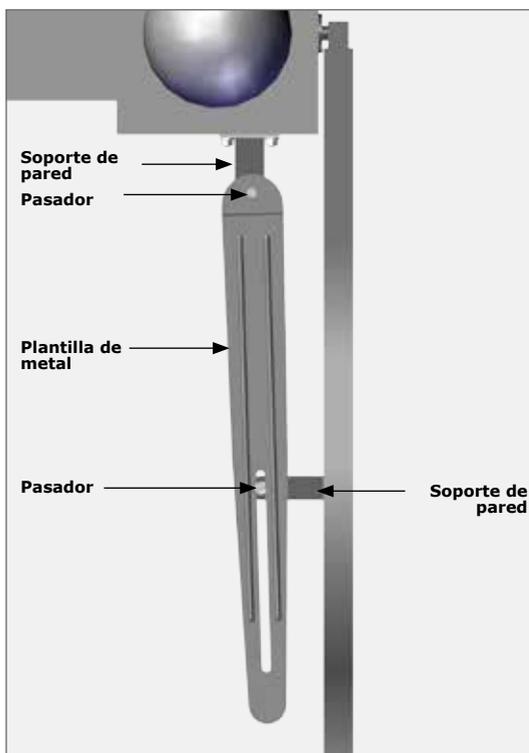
PORTÓN ABIERTO (PLANTILLA DE METAL MONTADA)
